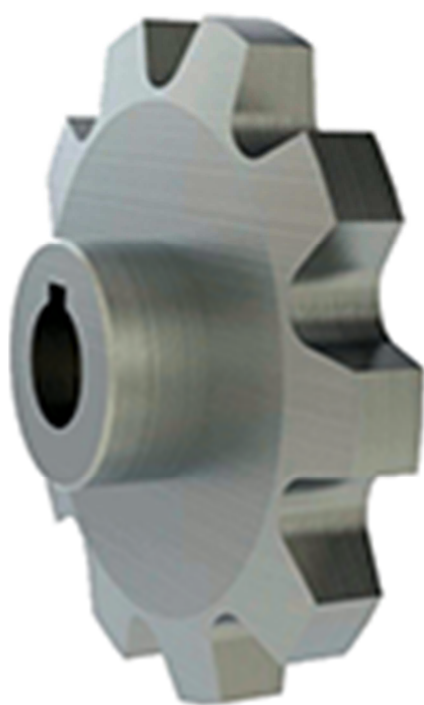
Звездочка для цепей транспортеров и элеваторов типа ТРД-38-5600
